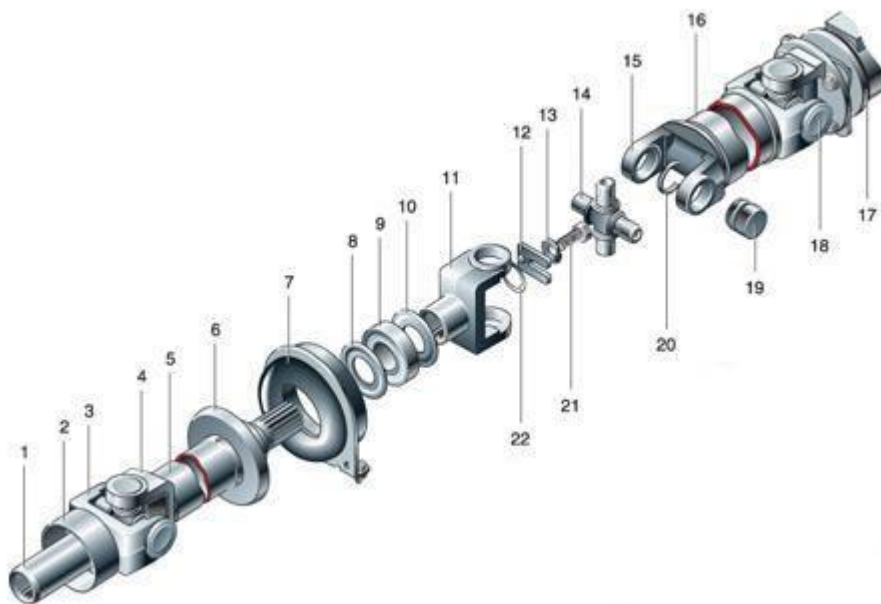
Схема карданной передачи автомобиля ГАЗ-3302 Газель [6]:
